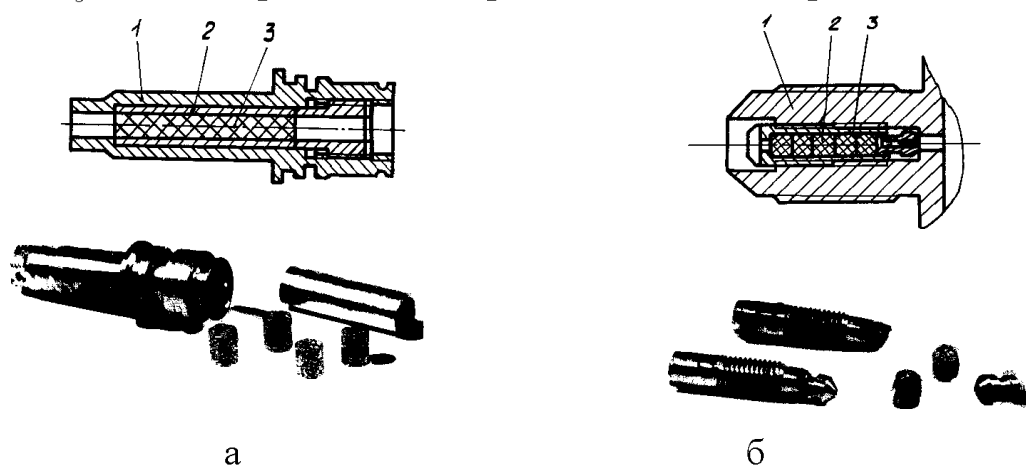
Конструктивная схема и внешний вид дроссельного пакета из материала МР для систем управления двигателя (а) и датчиков давления (б): 1 – корпус; 2 – втулка; 3 – дроссельный пакет
